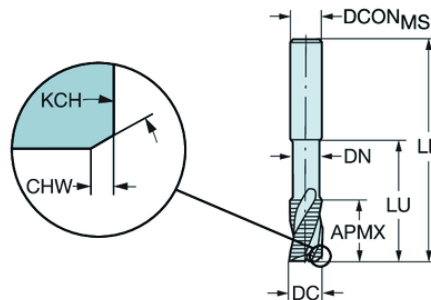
Фреза R216.33-25040-AJ20U H10F
